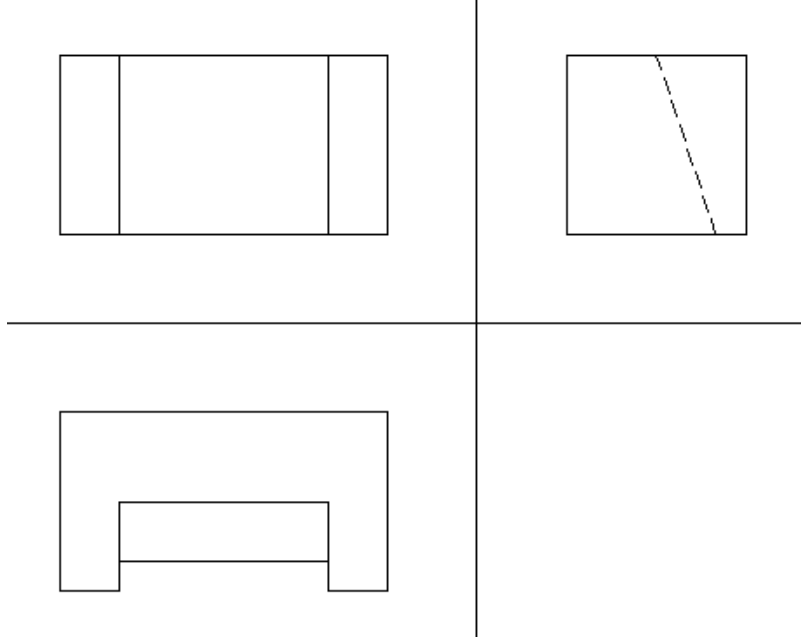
Temel boyutların profil düzlemine taşınması
